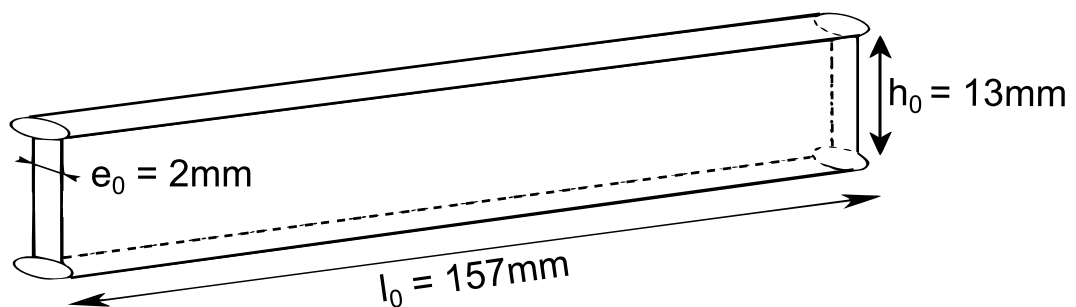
Géométrie et dimensions de l'éprouvette PS utilisée.
